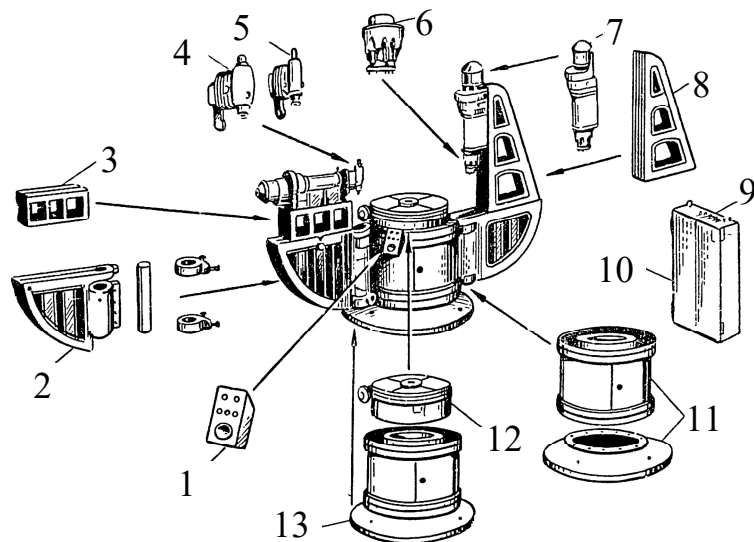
Компонування агрегатного верстата: 1 – пульт керування; 2 – горизонтальний кронштейн; 3 – проміжна плита; 4, 5 – фрезерувальні головки; 6 – багатошпindelна головка; 7 – силова бабка; 8 – вертикальний кронштейн; 9 – командо-апарат; 10 – електрошафа; 11, 13 – станина; 12 – ділильний стіл
